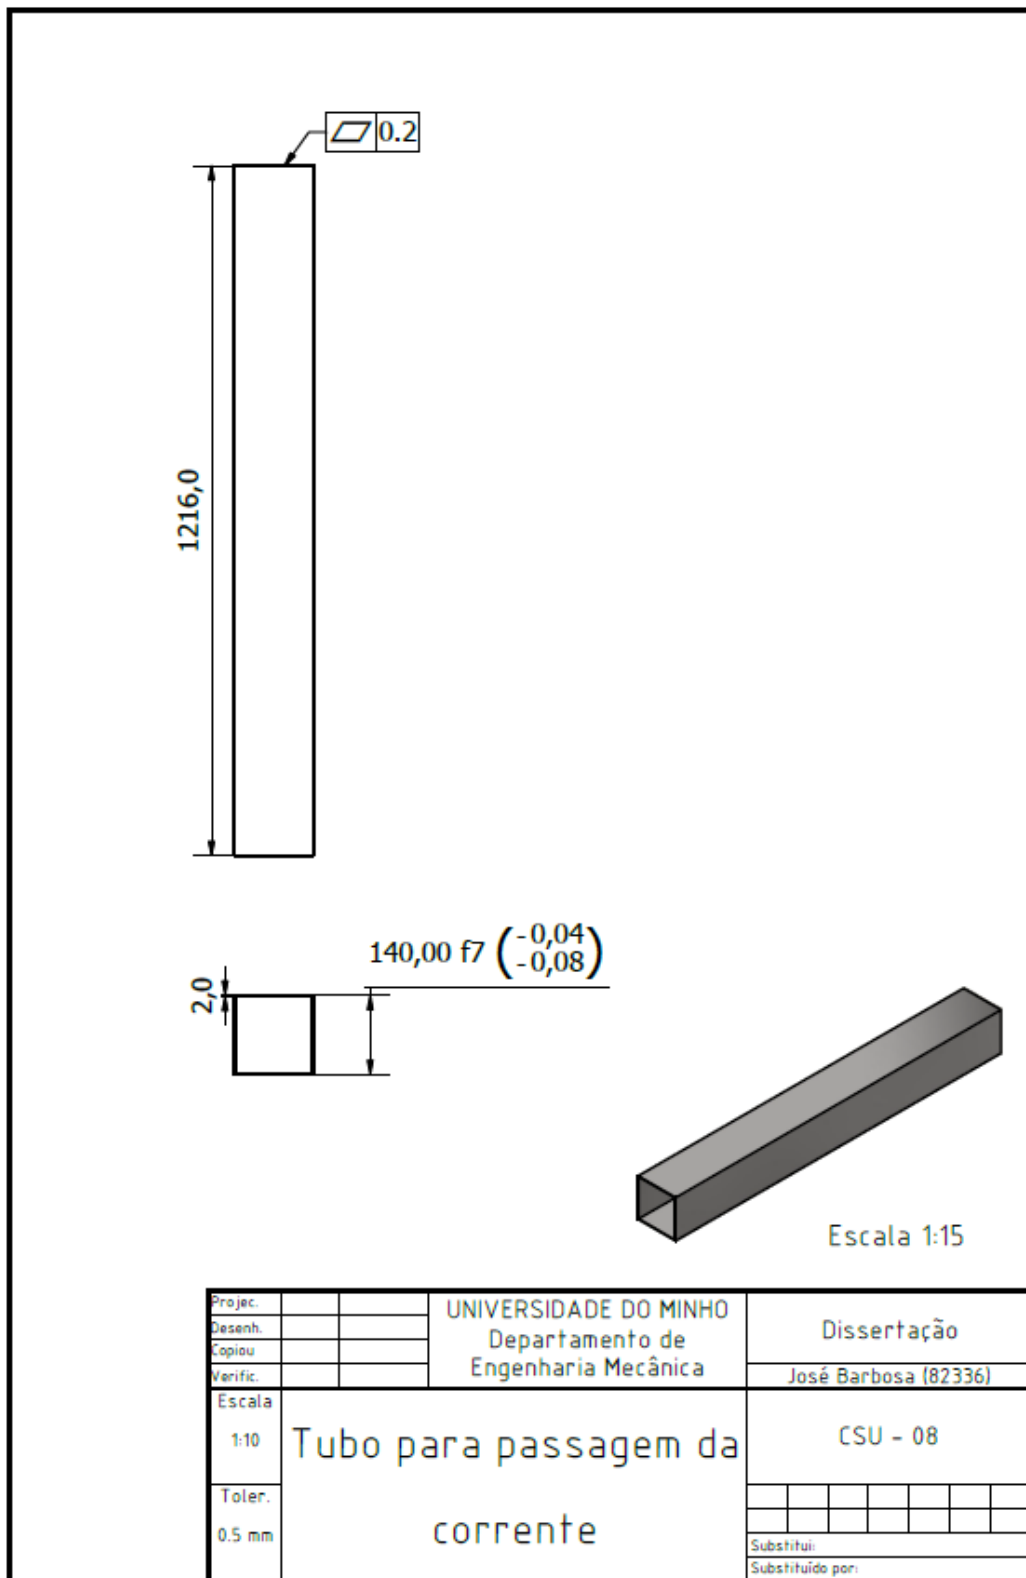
Figura Anexo III-11 – Desenho técnico do tubo para passagem da corrente.
